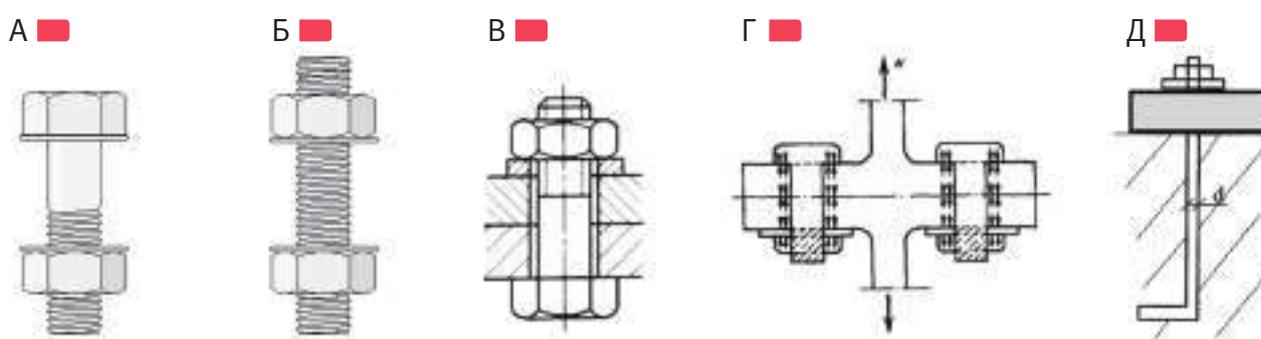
Схемы болтовых соединений: А – обычные болты; Б – шпильки; В – обычный болтовой пакет; Г – схема работы фрикционных болтов; Д – анкерный болт
